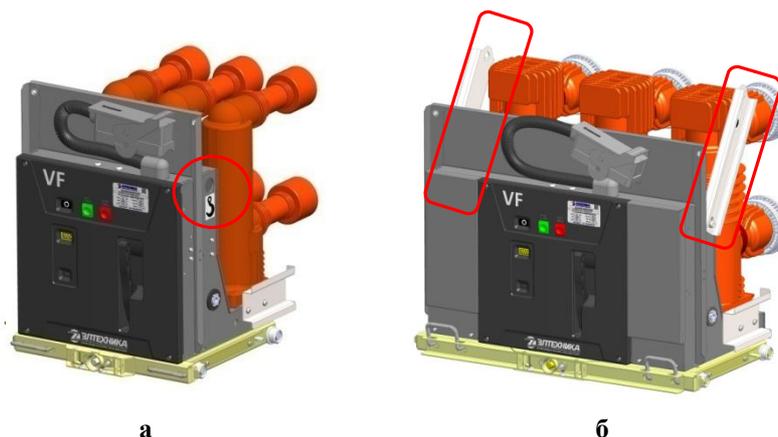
Расположение приспособлений для подъема выключателя: а – для выключателей на ток до 2500 А (с обеих сторон), б – для выключателей на ток 2500 и 3150 А
